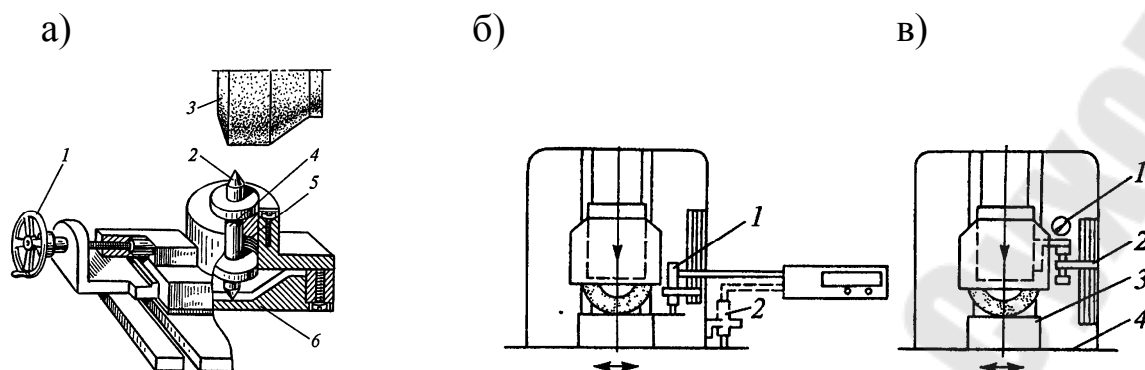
Универсальное приспособление для правки кругов на плоскошлифовальных станках (а) и способы контроля в процессе плоского шлифования (б – с помощью щупа; в – с помощью индикаторной головки)
